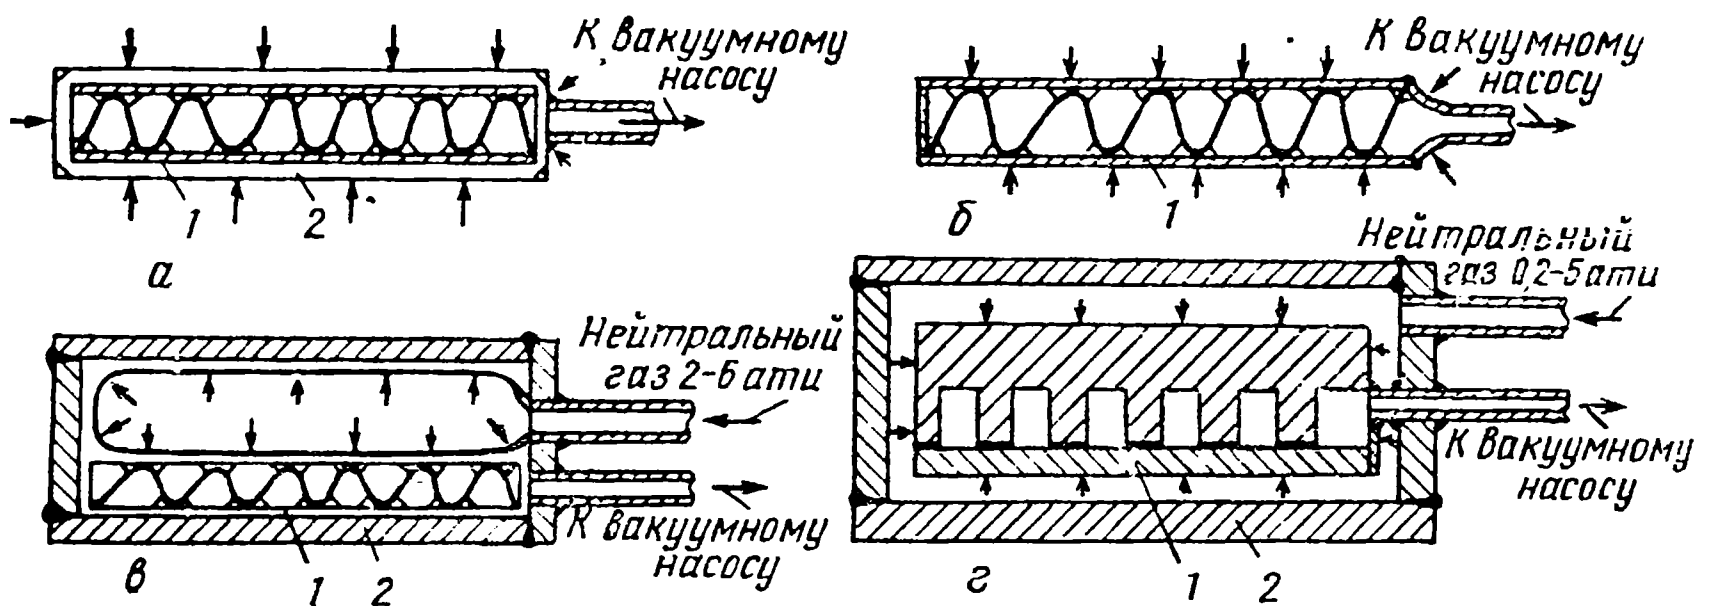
Приспособление для прижатия частей паяемых изделий с применением вакуума:
